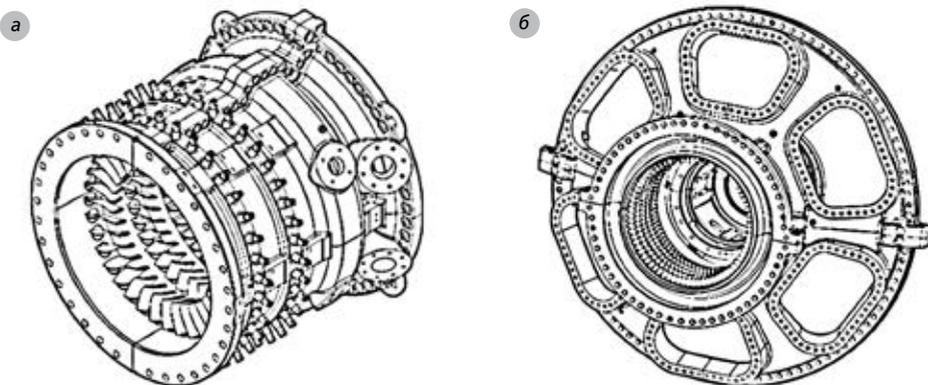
Общий вид корпусов осевого компрессора: а) входной корпус компрессора; б) выходной корпус компрессора
